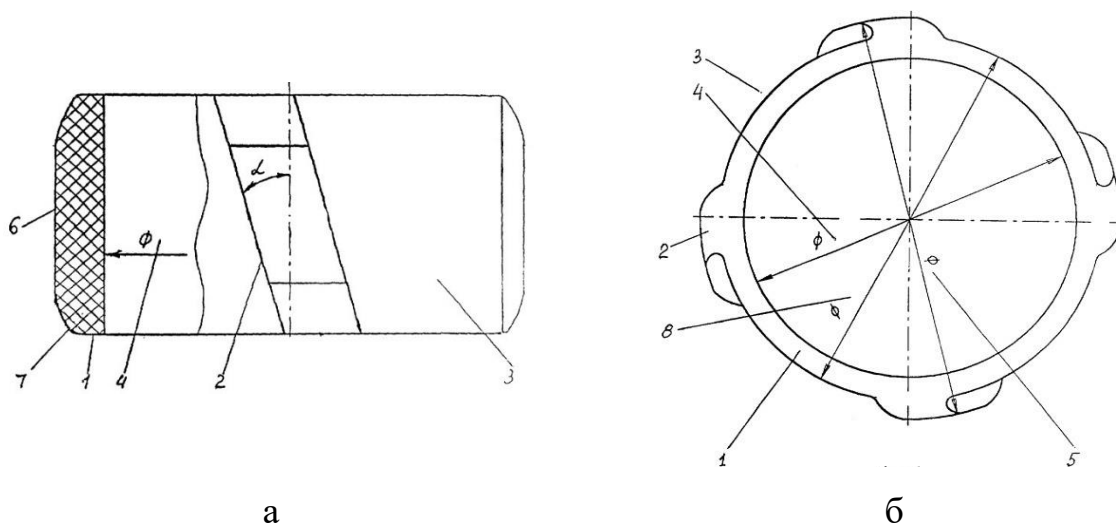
Полимерный центратор, а-общий вид центратора, б-вид сверху.
